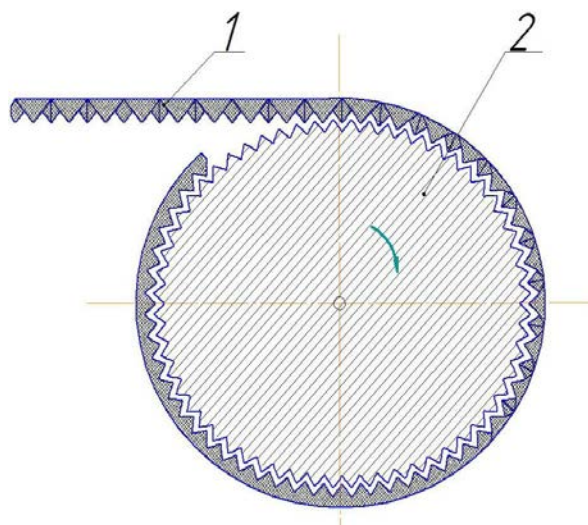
Сворачивание зубчатой ленты (флексагона) в спираль 1 – зубчатая лента, 2 – матрица (зубчатое колесо, конгруэнтное изготавливаемому венцу)
